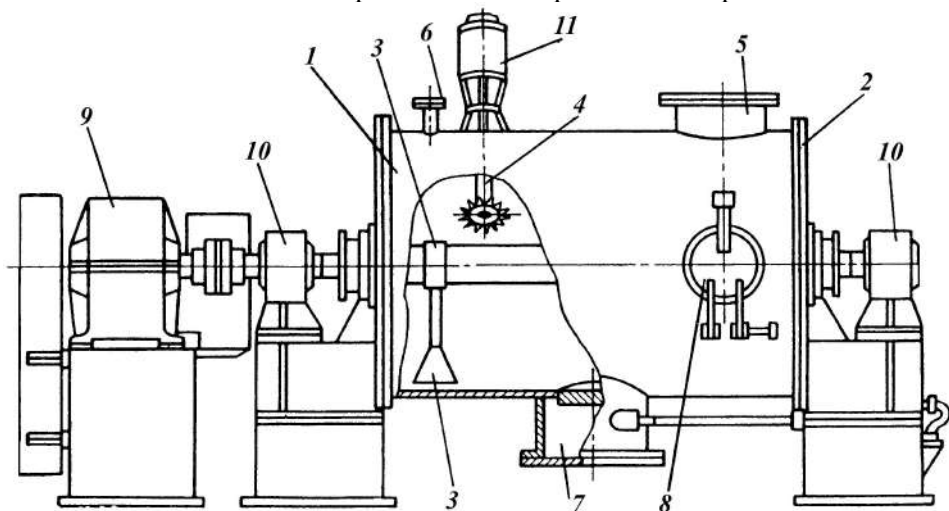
Смеситель плужный типа ПЖ: 1 – камера; 2 – крышка; 3 – лопасть; 4 – ножевая головка; 5 – загрузочный патрубок; 6 – штуцер; 7 – патрубок; 8 – люк; 9 – редуктор; 10 – подшипники качения; 11 – привод ножевой головки.
